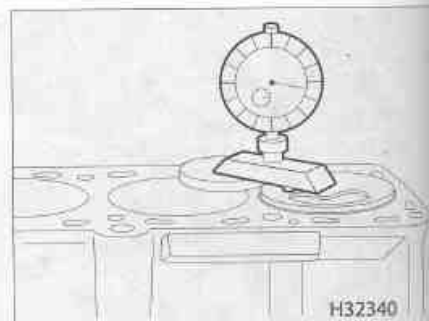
Измерение выступа поршня с помощью стрелочного индикатора
